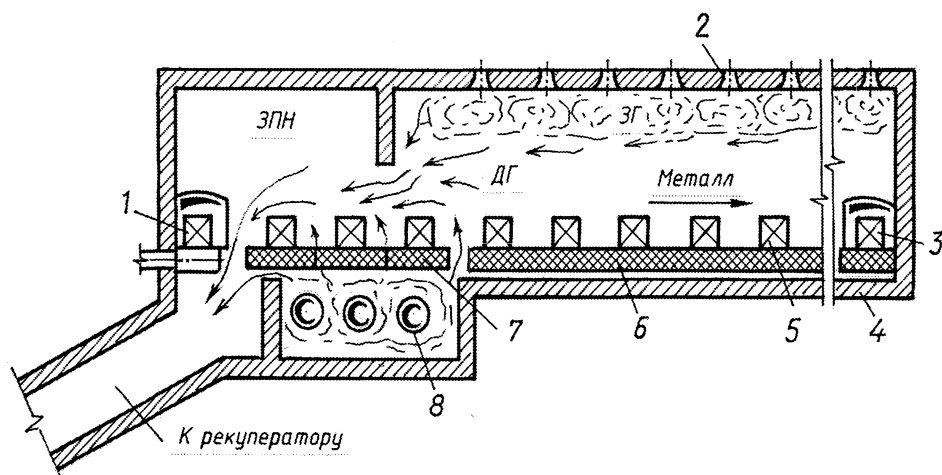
Схема нагревательной печи стана 320 РУП «БМЗ»: 1 – боковой посад заготовок; 2 – сводовая плоскопламенная горелка; 3 – боковая выдача заготовок; 4 – обмуровка печи; 5 – нагреваемая заготовка; 6 – участок шагающего пода; 7 – шагающие балки; 8 – боковая длиннофакельная горелка; ЗПН – зона предварительного нагрева; ЗГ – зона горения; ДГ – дымовые газы
